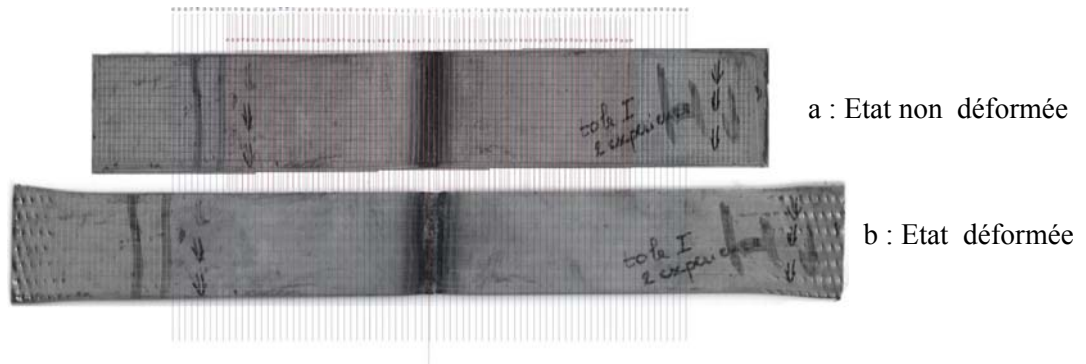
Eprouvette soudée déformée à 27%
